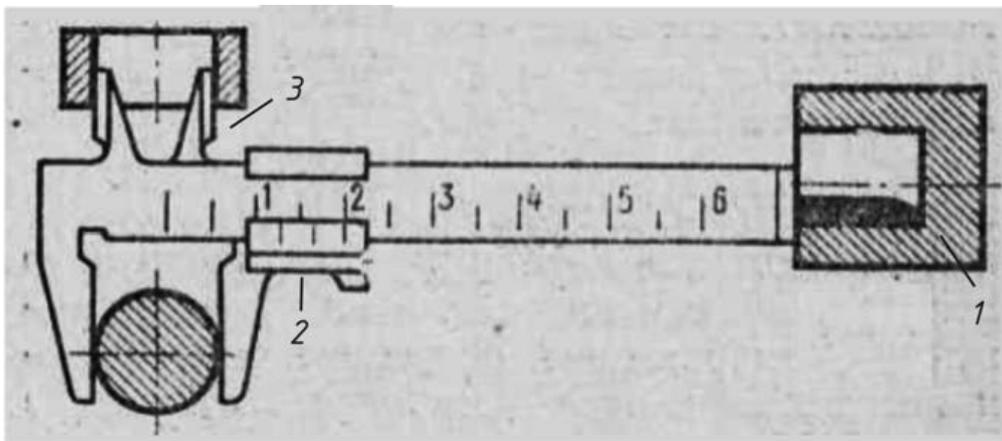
Штангенциркуль: 1 — глубиномер; 2 — нониус; 3 — ножки
